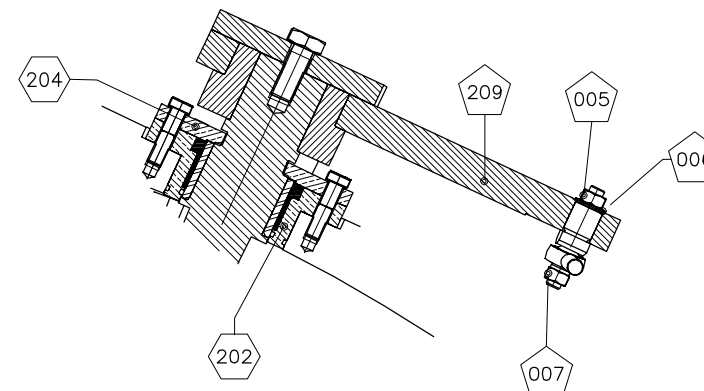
DETAIL RADIÁLNÍHO ČEPU LOPATKY
